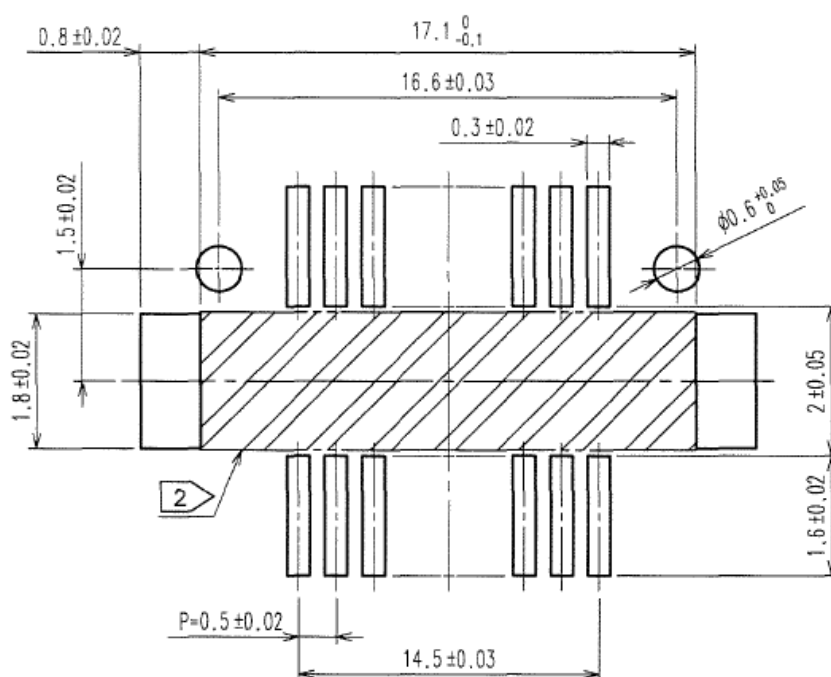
MC703 模块上使用的连接器焊盘尺寸 (单位: mm)
